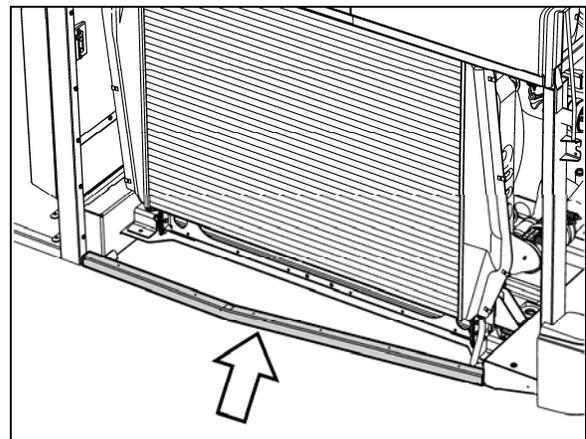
PROTECTEUR DU TUBE DE L'ENSEMBLE RADIATEUR INFÉRIEUR
